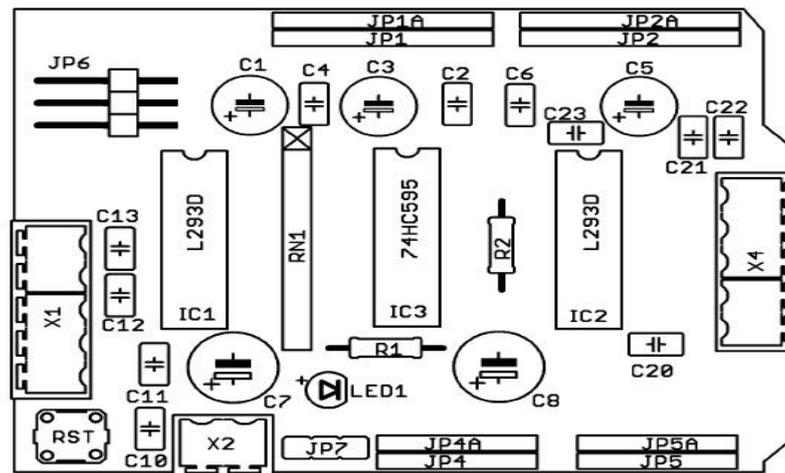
Схема сборки Motor Shield v2 Kit
